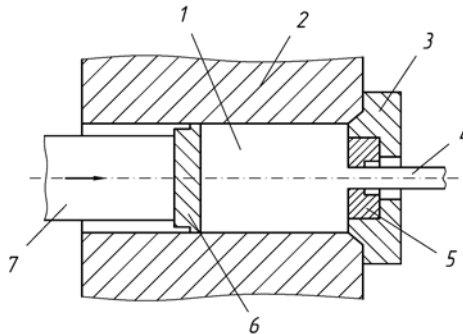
Оснастка для прессования: 1 – заготовка, 2 – контейнер, 3 – матрицедержатель, 4 – изделие, 5 – матрица, 6 – пресс-шайба, 7 – пресс-штемпель
